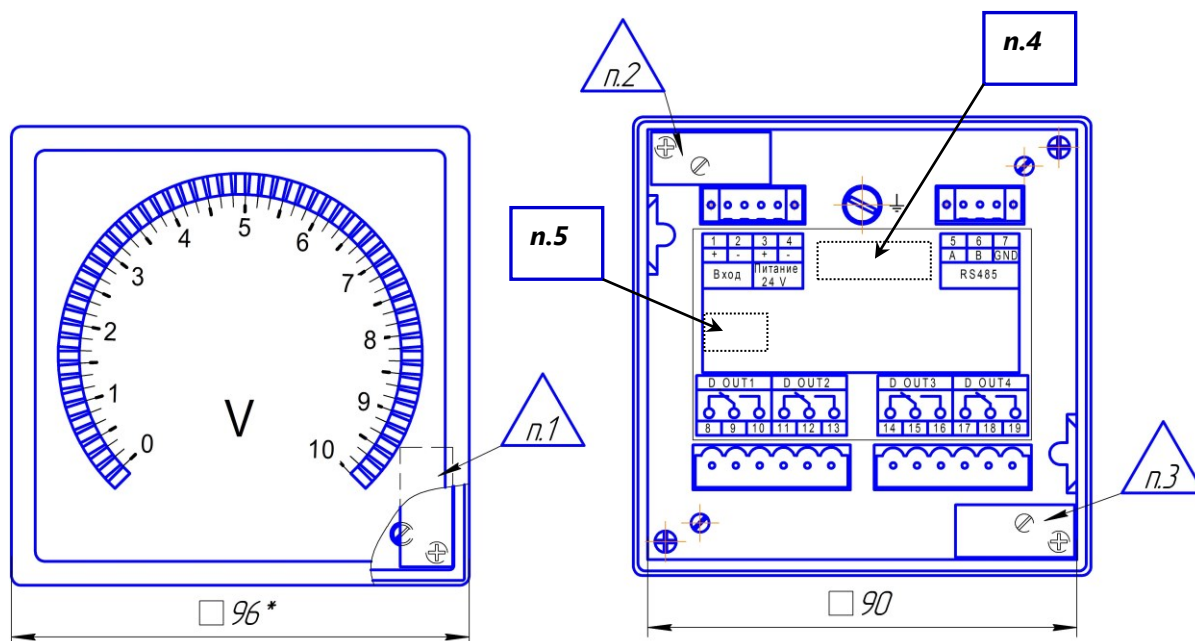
Общий вид приборов Щ23.7, Щ23.8
